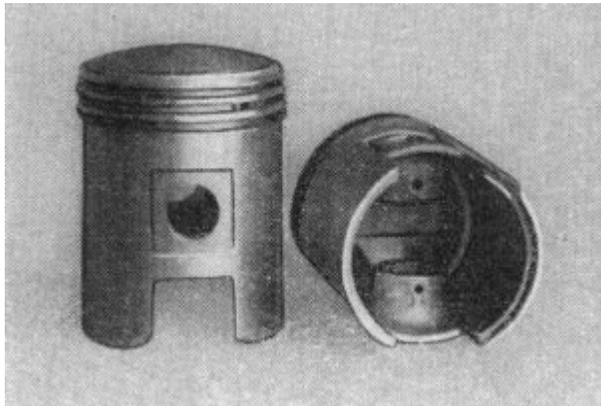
Die beiden genau gleichen Kolben aus Leichtmetall
